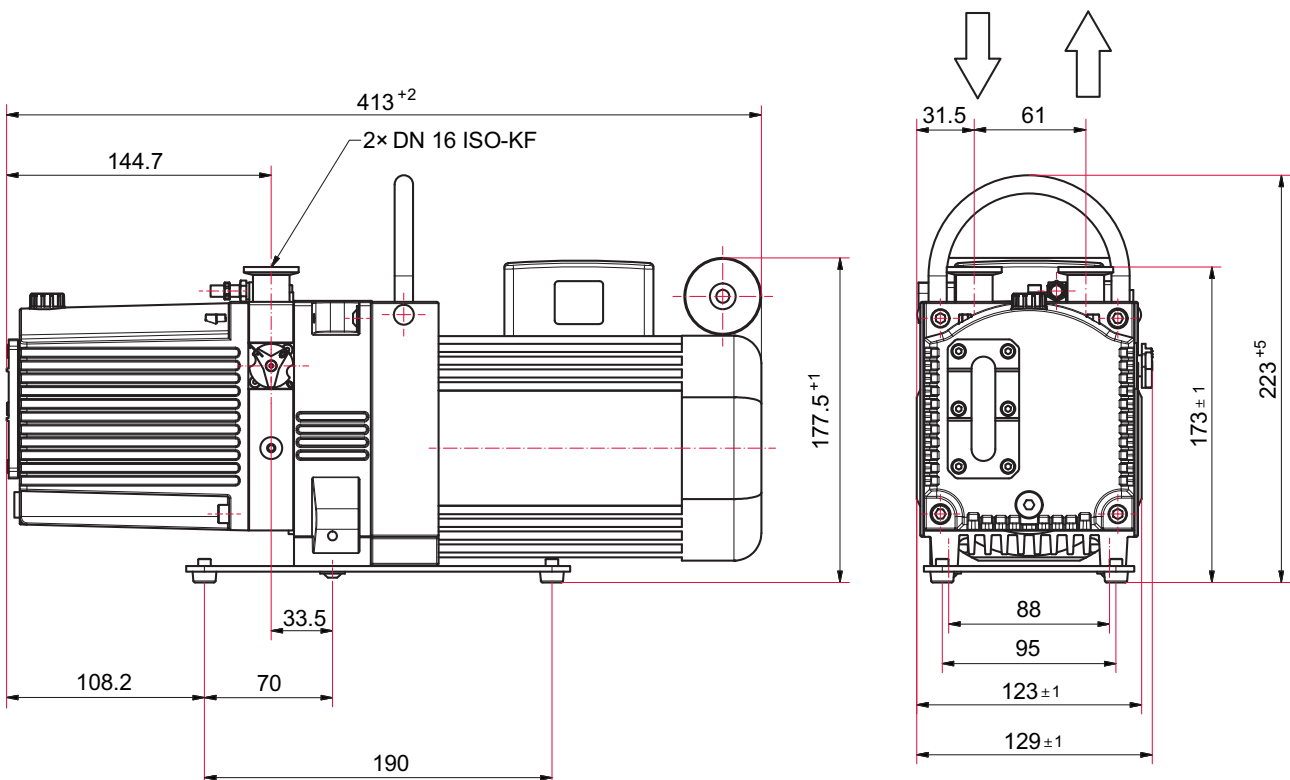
Dimensões do Duo 6 M, motor monofásico, 230–240 V, 50/60 Hz
